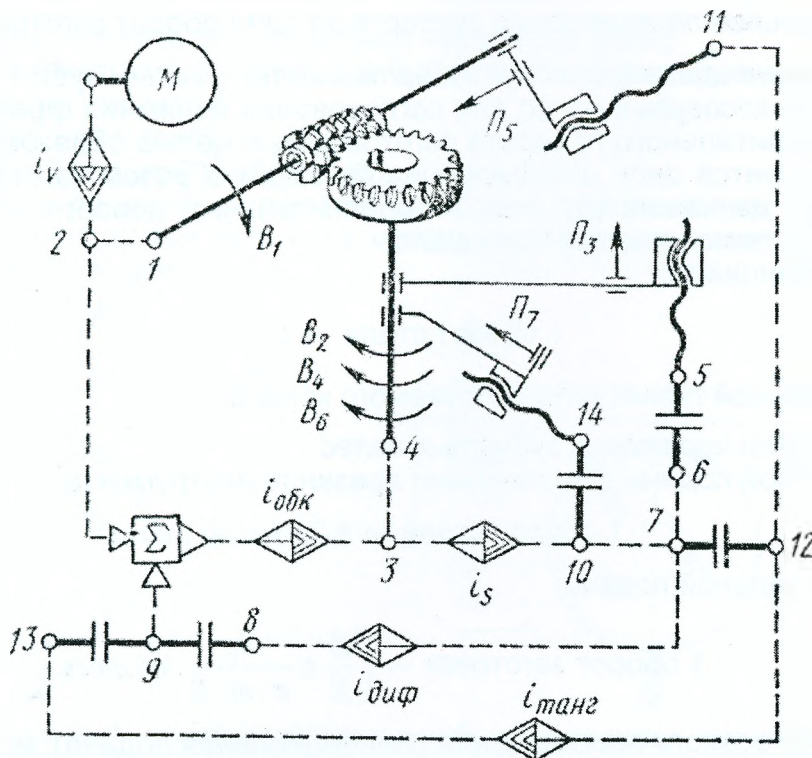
Кинематическая структура зубофрезерного станка:
